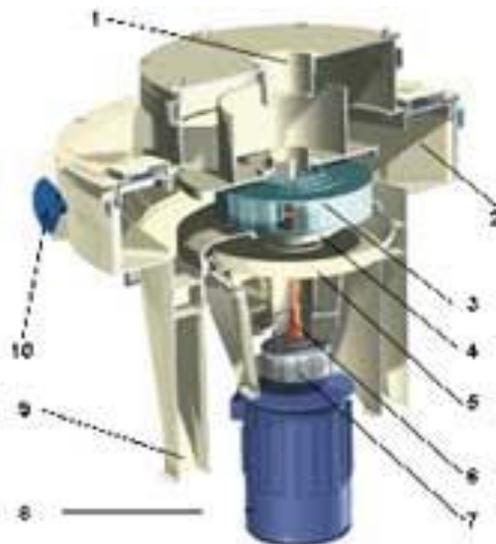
Схема дробилки «Титан Д»: 1 - загрузочная воронка; 2 - камера дробления с самофутеровкой; 3 – ускоритель; 4 - демпферный узел; 5 - воздушная опора; 6 - карданный вал; 7 - центробежная муфта; 8 – электродвигатель; 9 - разгрузка дробленого материала; 10 - вентилятор наддува
